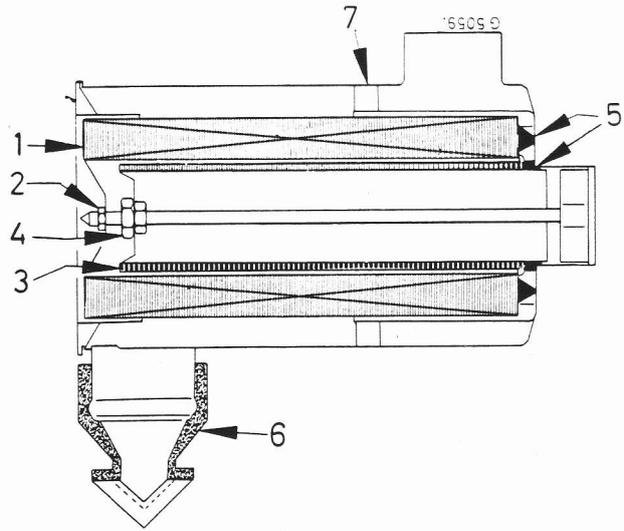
Vue en coupe du filtre à air sec à double étage.
